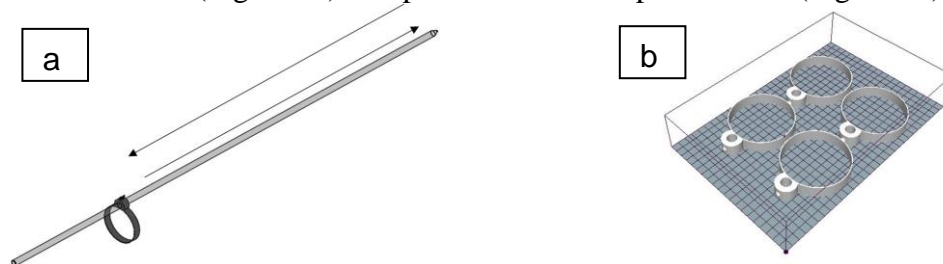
Figura a) suporte com regulagem de altura, vista isométrica, figura b) mesa de impressão 3D com a impressão dos suportes.
